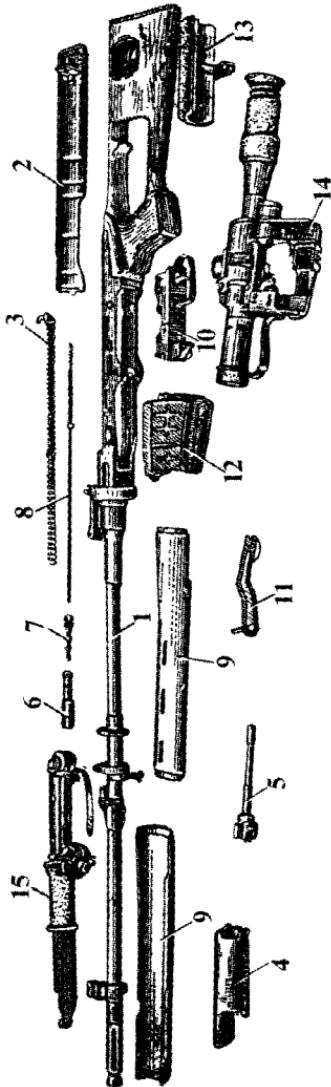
Основные части и механизмы СВД-63: 1 – ствол со ствольной коробкой, открытым прицелом и приспособлением; 2 – крышка ствольной коробки; 3 – возвратный механизм; 4 – газовая рама; 5 – затвор; 6 – газовая трубка; 7 – газовый поршень; 8 – толкатель с пружиной; 9 – толкатель с пружиной; 10 – ударно-спусковой механизм; 11 – предохранитель; 12 – магазин; 13 – щека приклада; 14 – оптический прицел; 15 – штык-нож.
